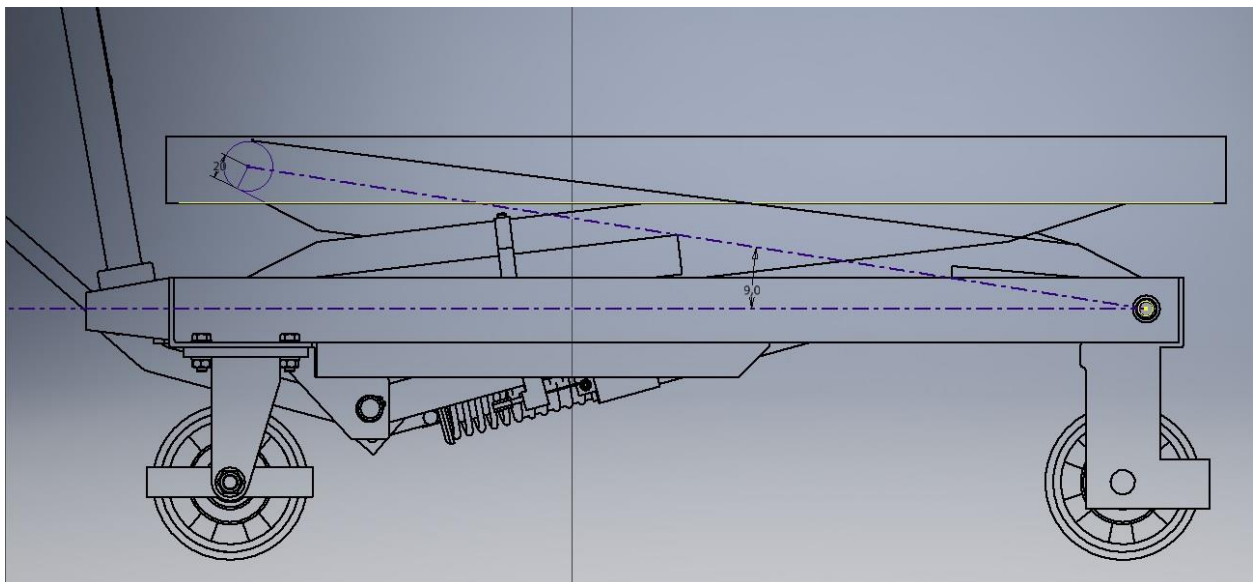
Kut cilindra u odnosu na horizontalnu površinu u izdignutom položaju platforme
